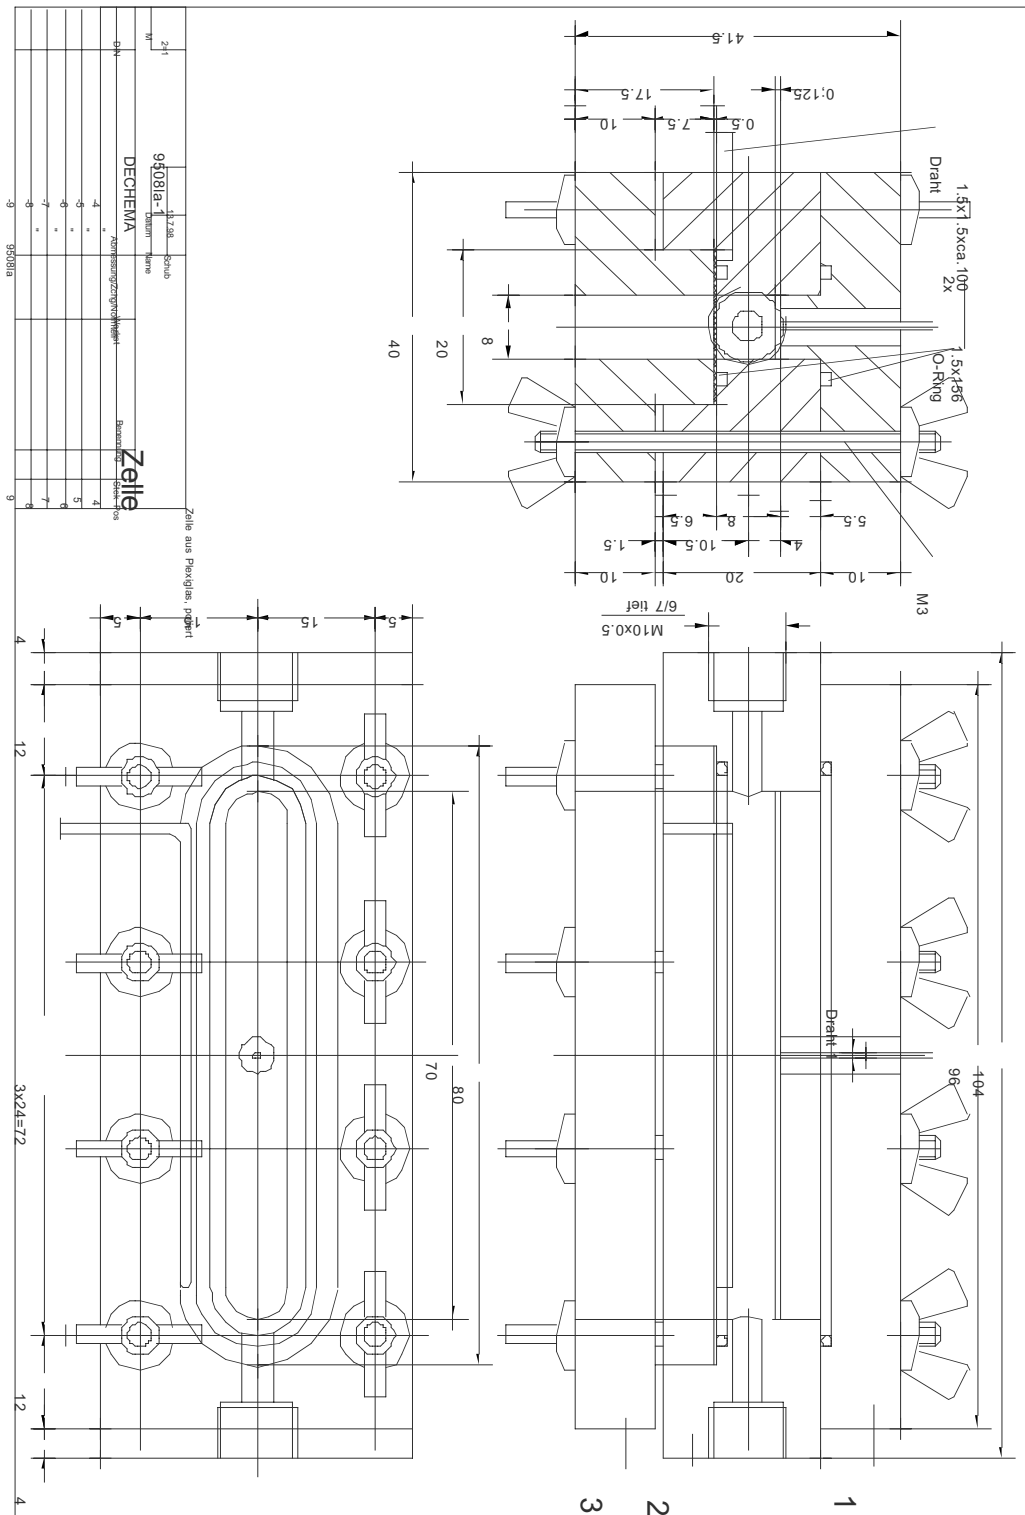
Technische Zeichnung der Biobrennstoffzelle (Gesamtansicht)
